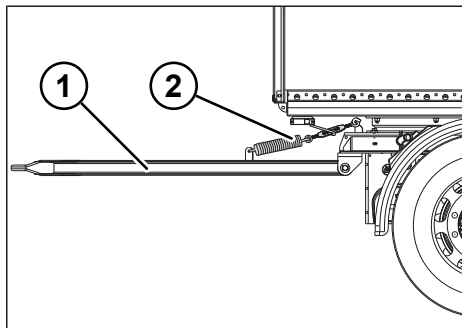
Тяговая вилка с устройством для регулировки высоты
